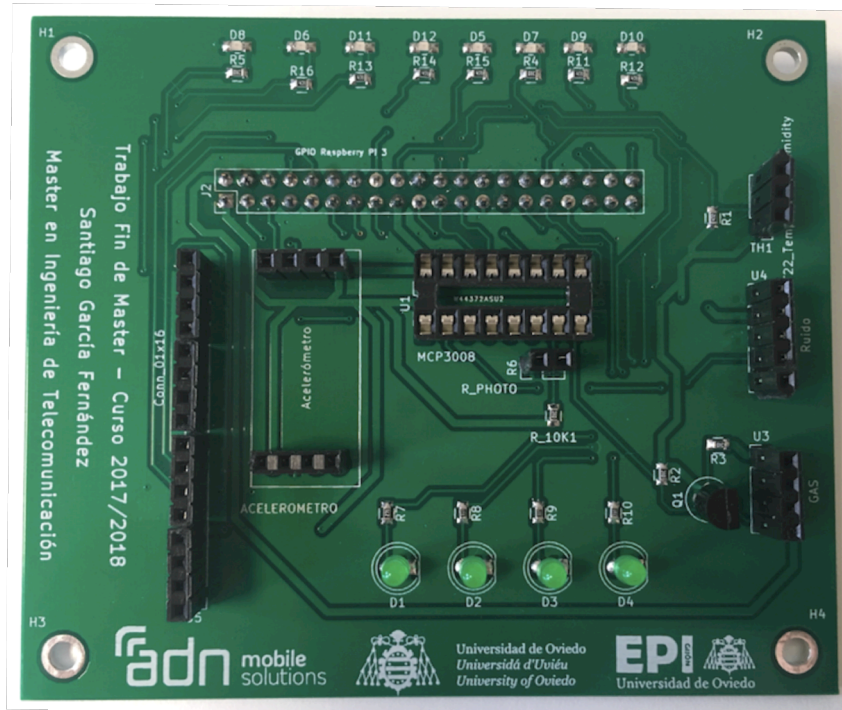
Imagen de capa top de la PCB real una vez se han soldado los diferentes componentes sobre la placa.
